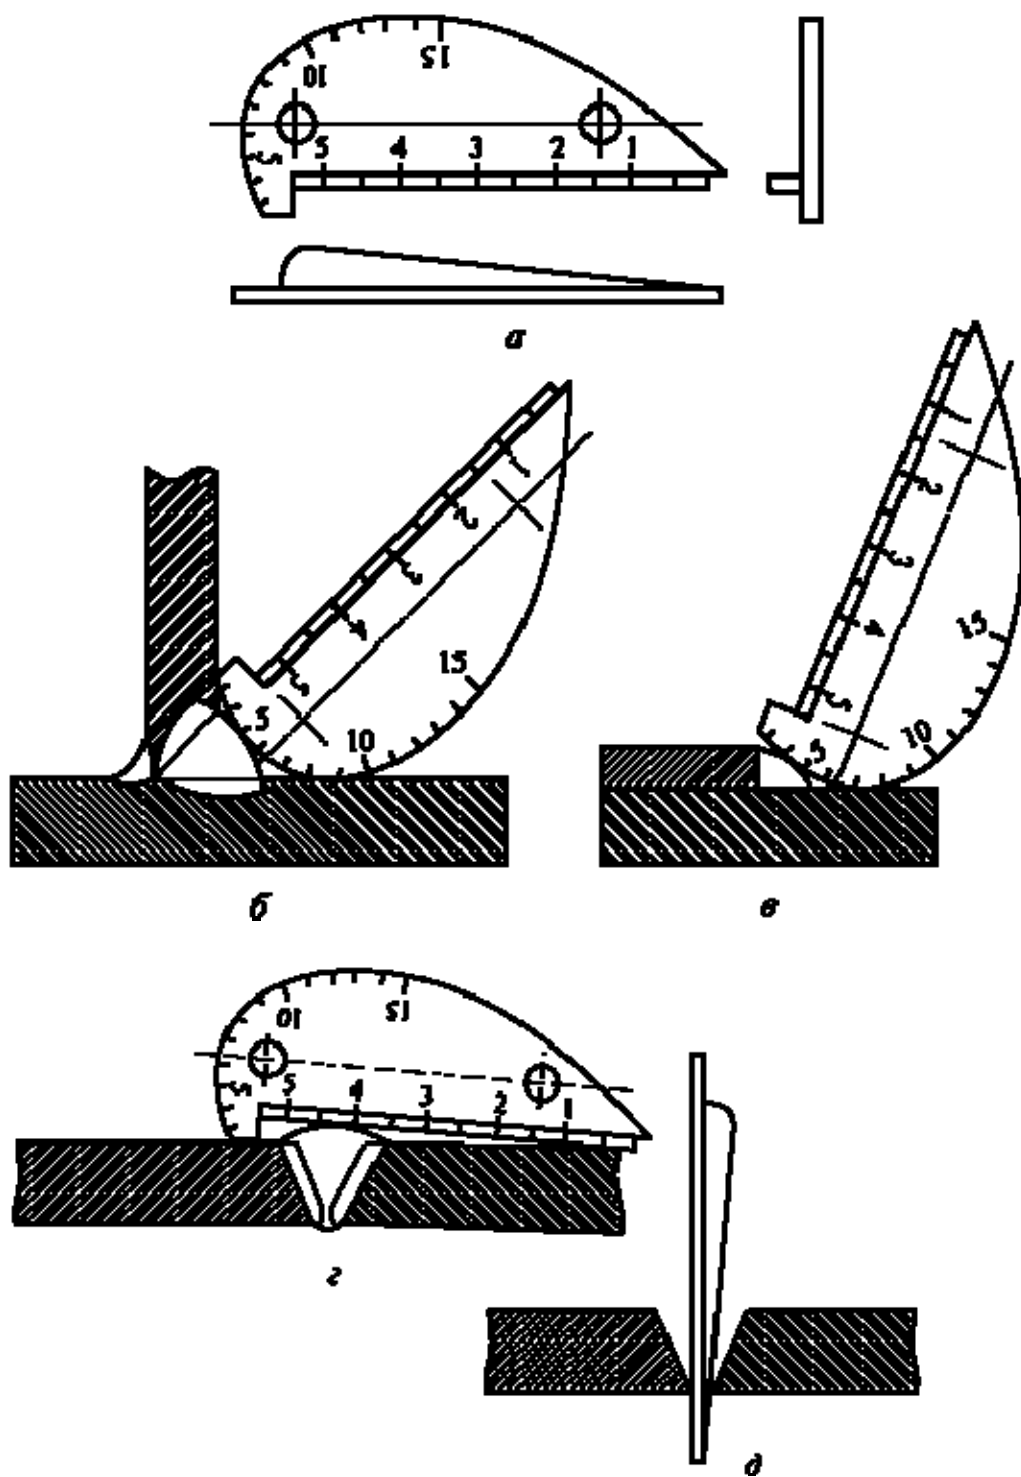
Контроль универсальным шаблоном сварщика УШС
